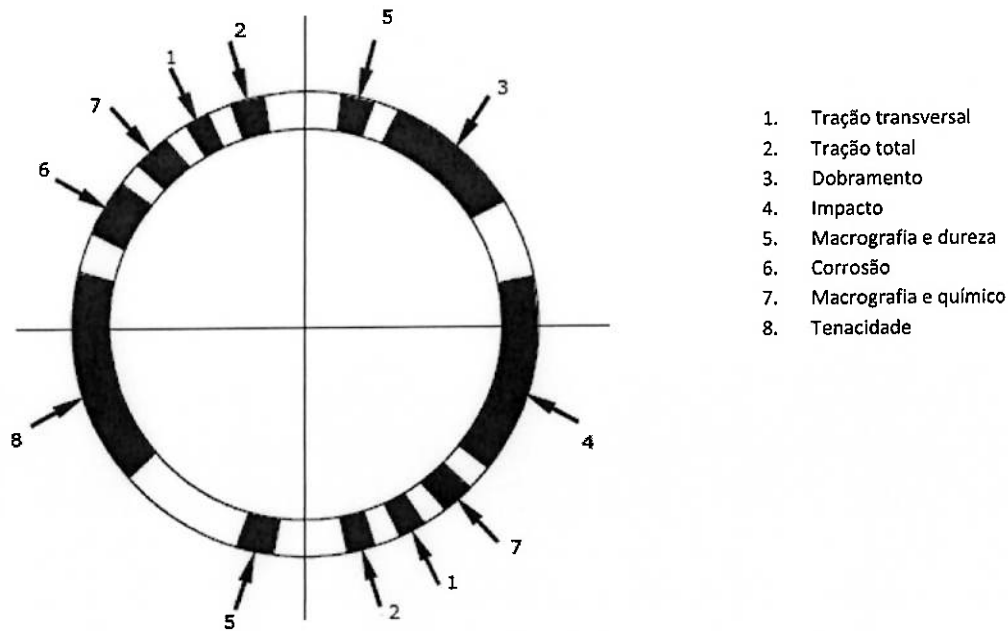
Locais para a retirada de corpos de prova para ensaios de qualificação de soldagem, conforme a DNV-OS-F101 [10].
